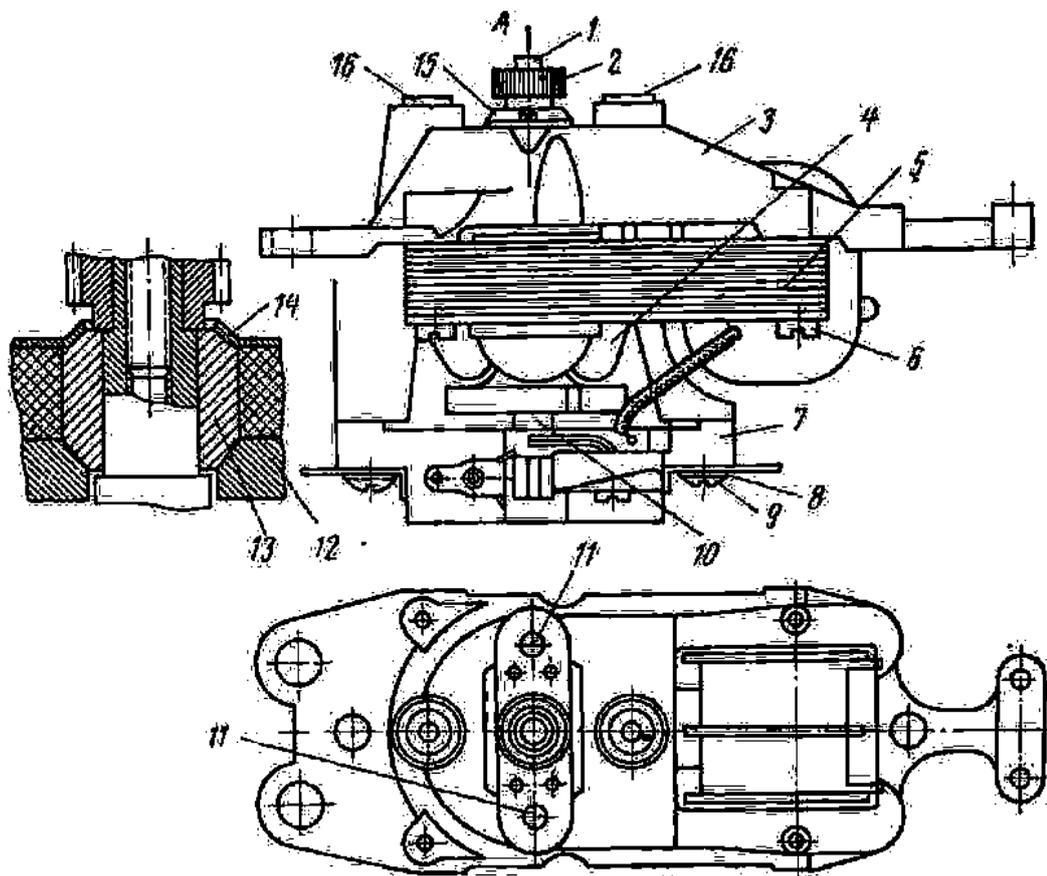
Электродвигатель бритвы «Москва» ИП-6: 1. 6. 9 к 11—винты; 2 — шестерня; 3 — каркас; 4 — якорь; 5 — статор с катушкой; 7 — колодка; 6 — шайба; 10 — щетка угольная; 12 и 15 — прокладки; 13 и 16 — подшипники; 14 — держатель
